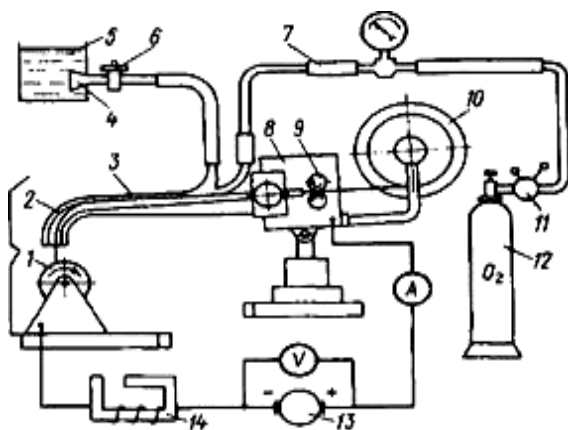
Схема установки для вибродуговой наплавки в газожидкостной среде:
